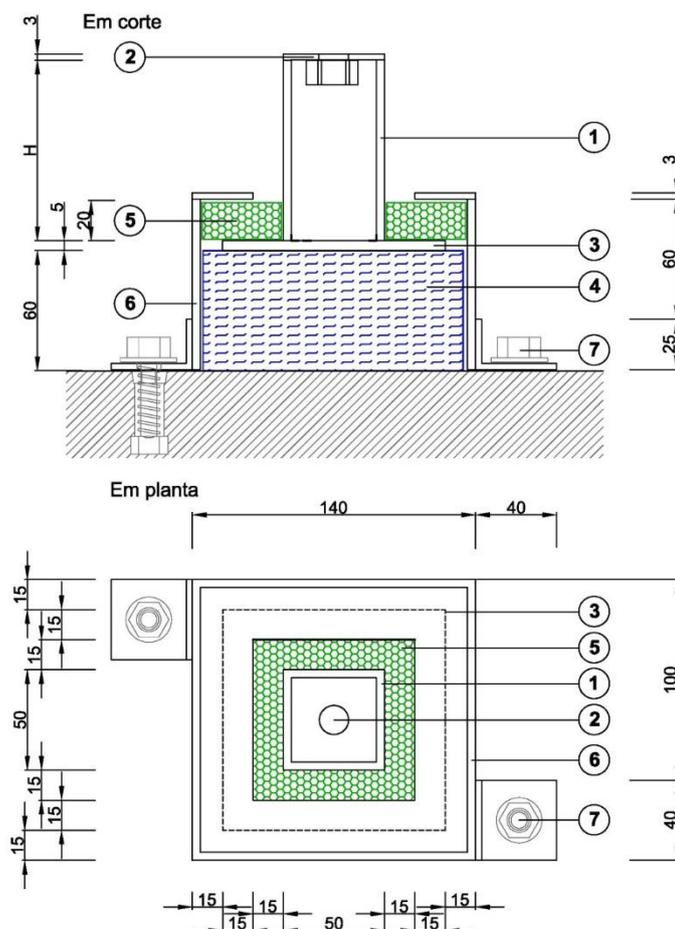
Desenho técnico do apoio antivibratório e antissísmico (com as dimensões indicadas em mm).
